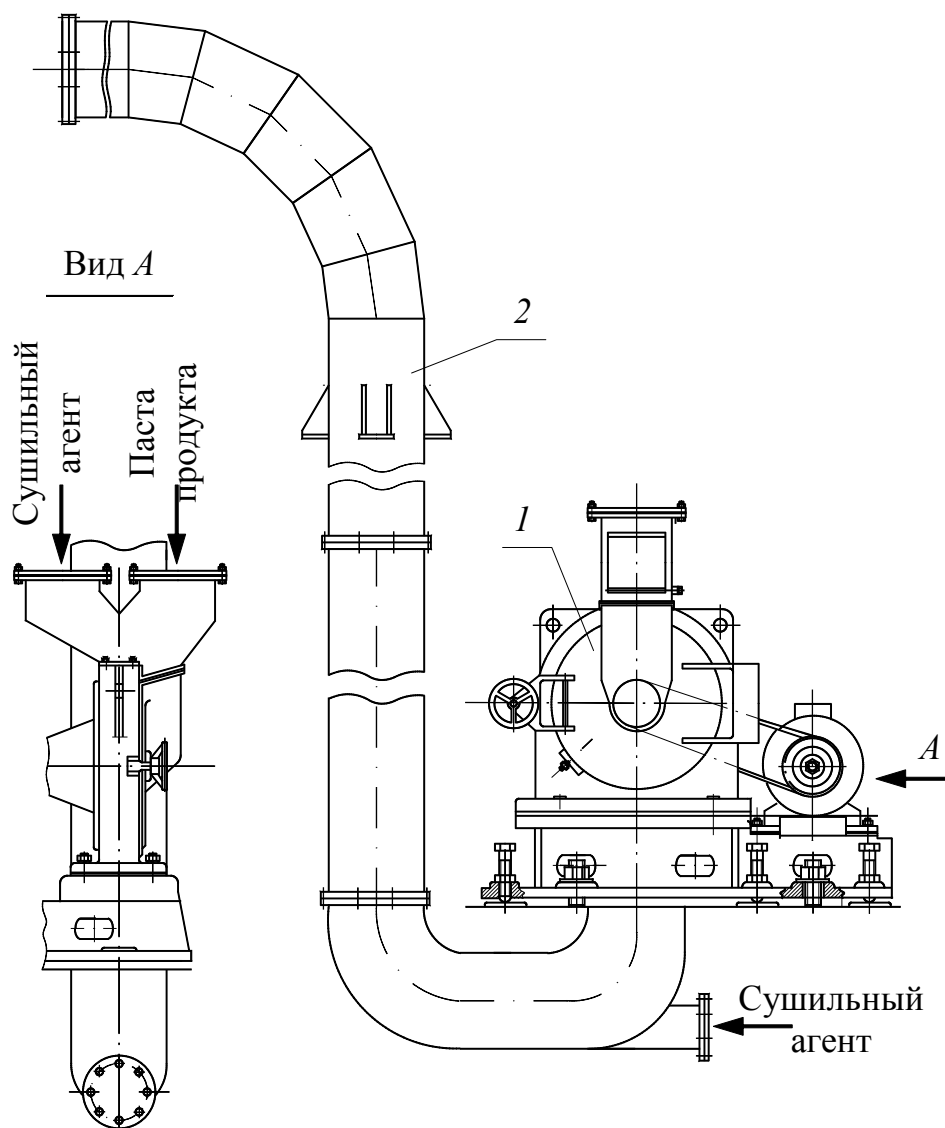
Пневматическая сушилка на базе дисмембратора:
